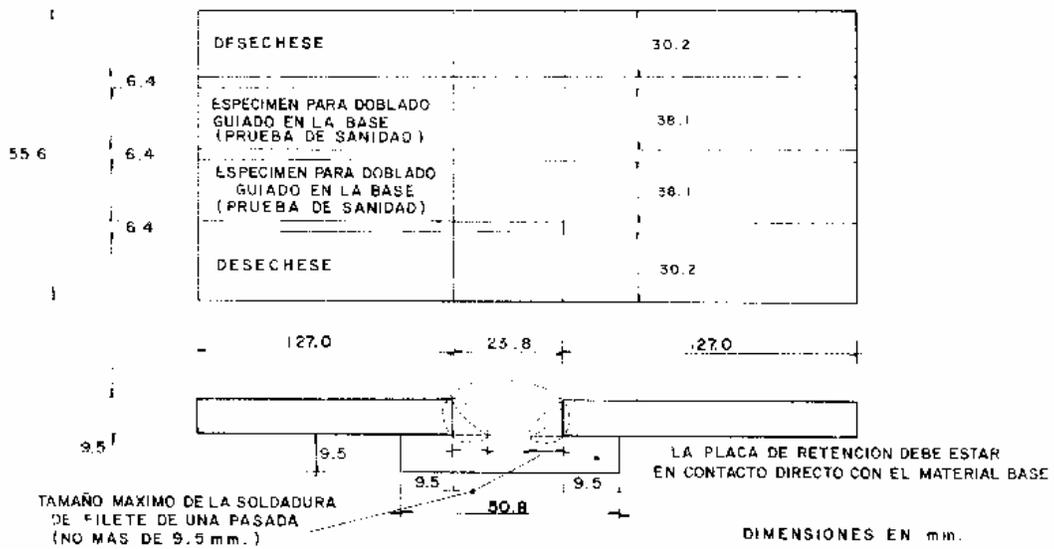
SOLDADURA DE ENSAYO PARA PRUEBAS DE SANIDAD (UNICAMENTE PARA CALIFICACION DE SOLDADORES)
